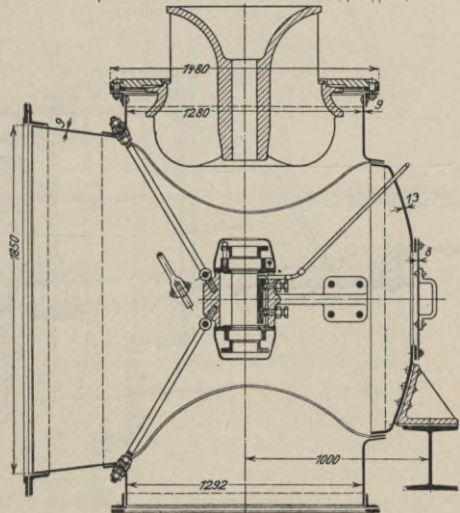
Querschnitt durch d. Laufrad d. Francis-Turbine.
